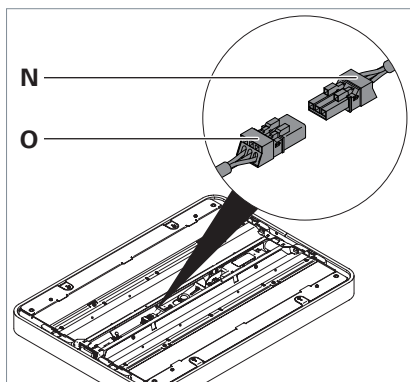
Collegamento della testa dell'apparecchio d'illuminazione, parte 2.
